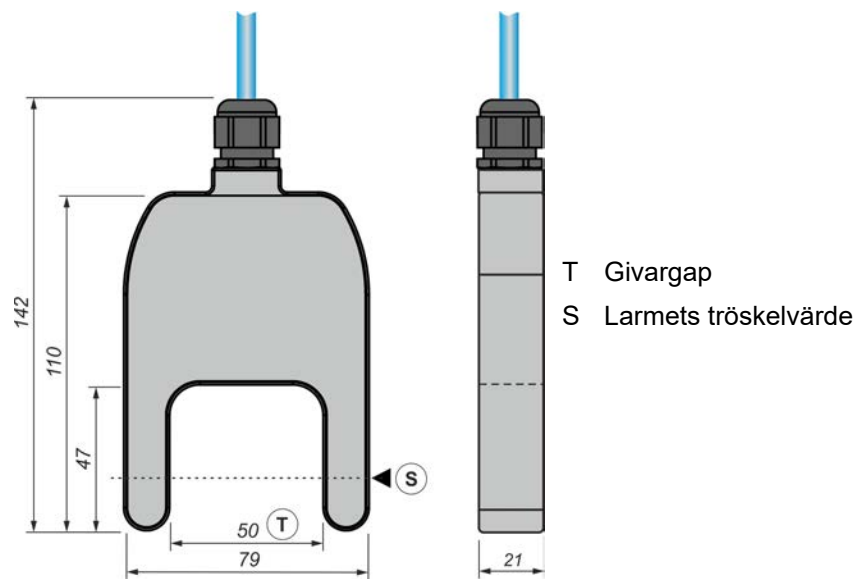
Slamgivare idOil-SLU – struktur och mått (mm)
